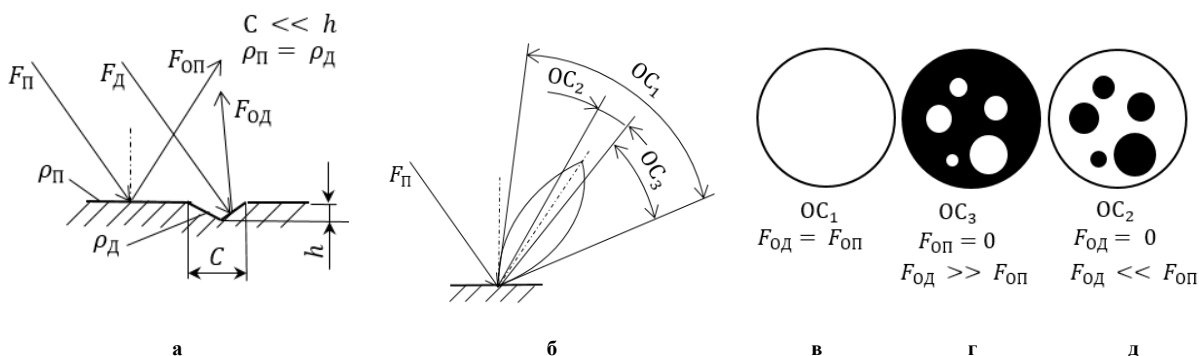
Зображення робочої поверхні ріжучої пластини з пластичними мікрodefектами
